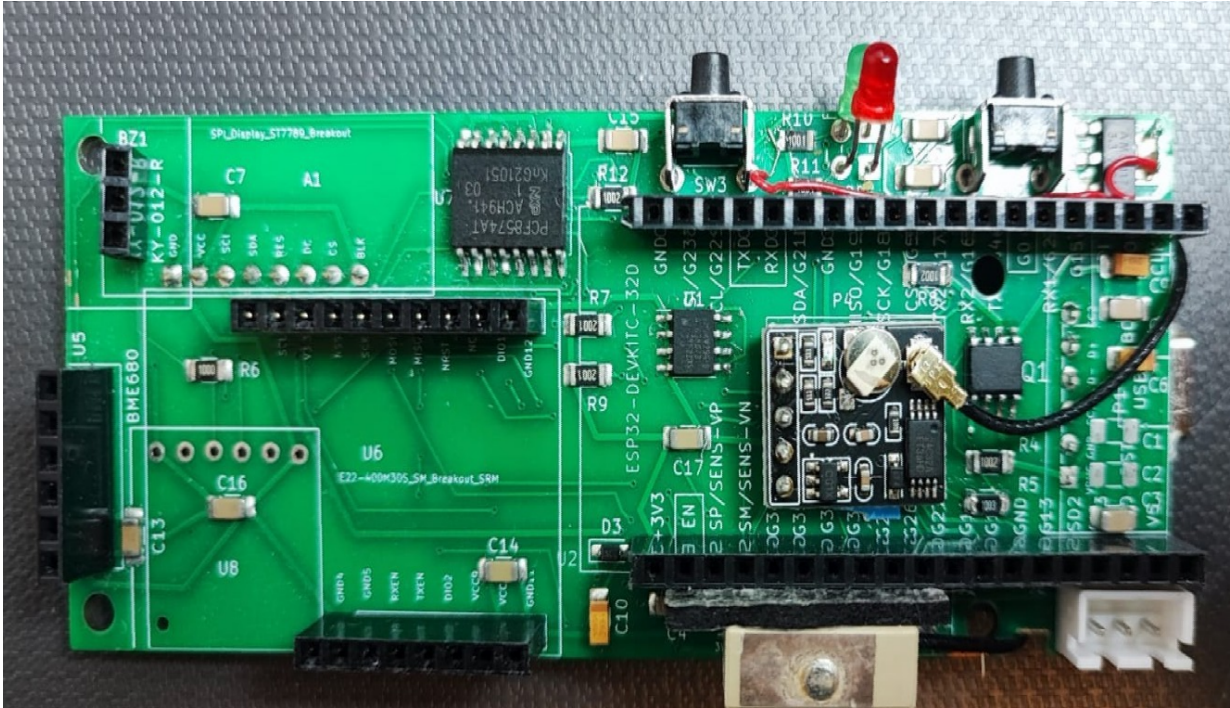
PCB Mini senza moduli ad innesto a montaggio ultimato.
